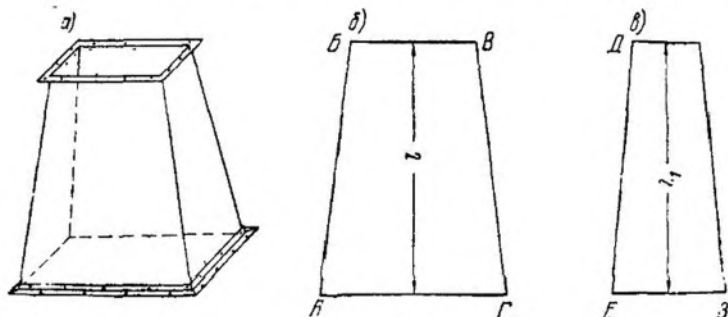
Развертка перехода с прямоугольного на прямоугольное сечение
